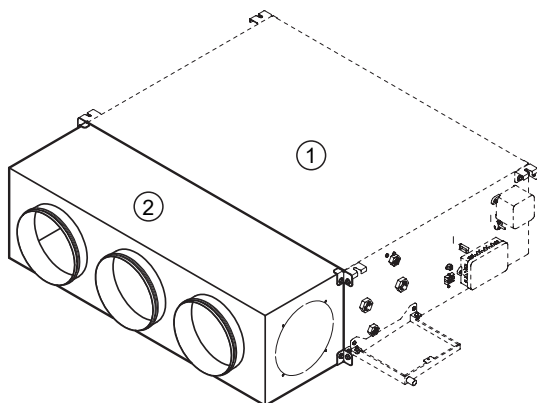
Основной прибор с соединительным элементом для круглой трубы
